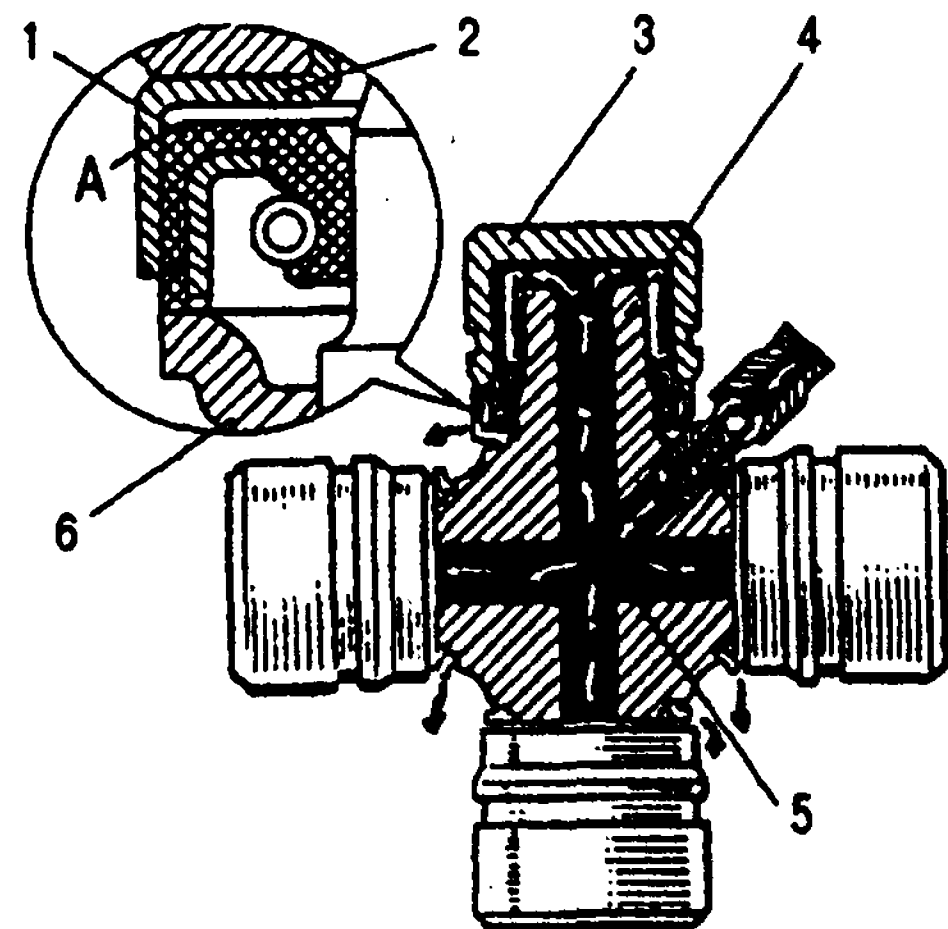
Схема смазки подшипников карданного шарнира: 1 - манжета; 2 - обойма манжеты; 3 - игольчатый подшипник; 4 - крестовина; 5 - масляные каналы; 6 - грязеотражатель; А - фаска манжеты
